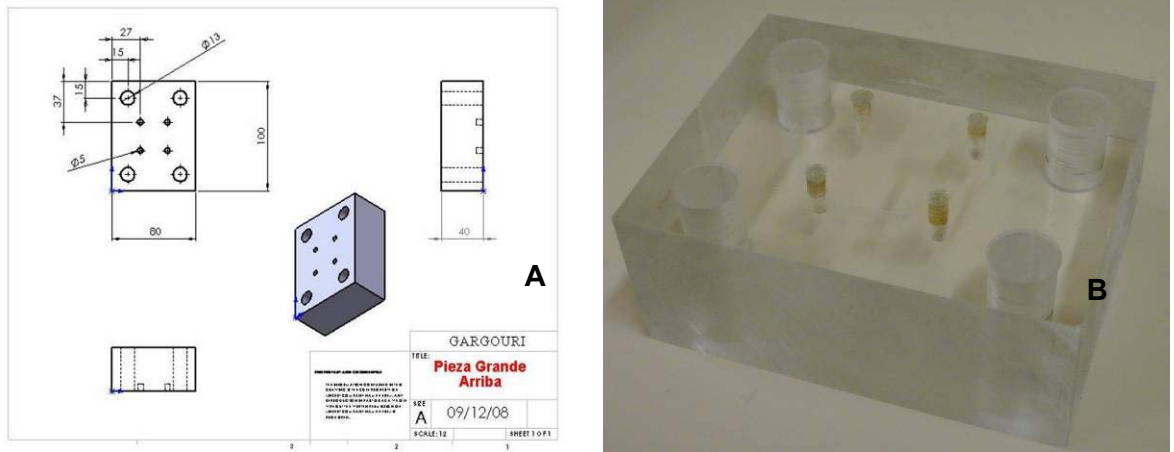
(A) Vistas y dimensiones de una de las piezas del montaje: pieza grande arriba, (B) Foto de la pieza grande arriba.
